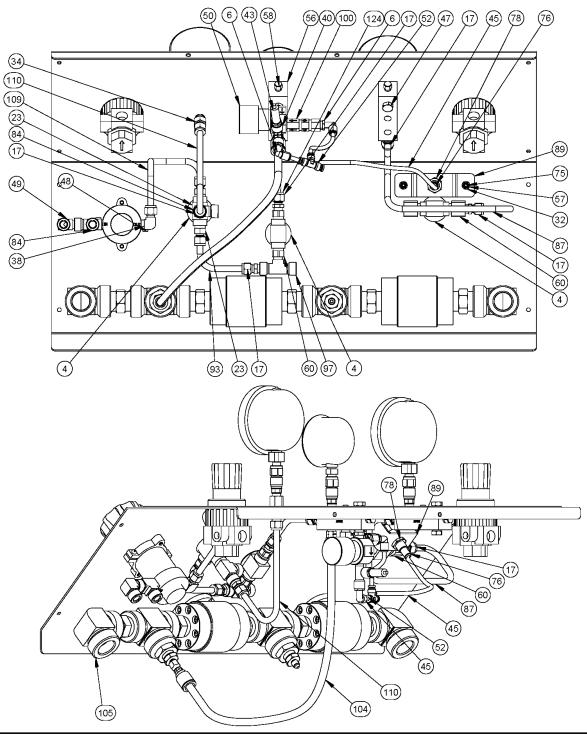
DETALLES B Y C DE MONTAJE DE LA CONSOLA (N/P 97861)
